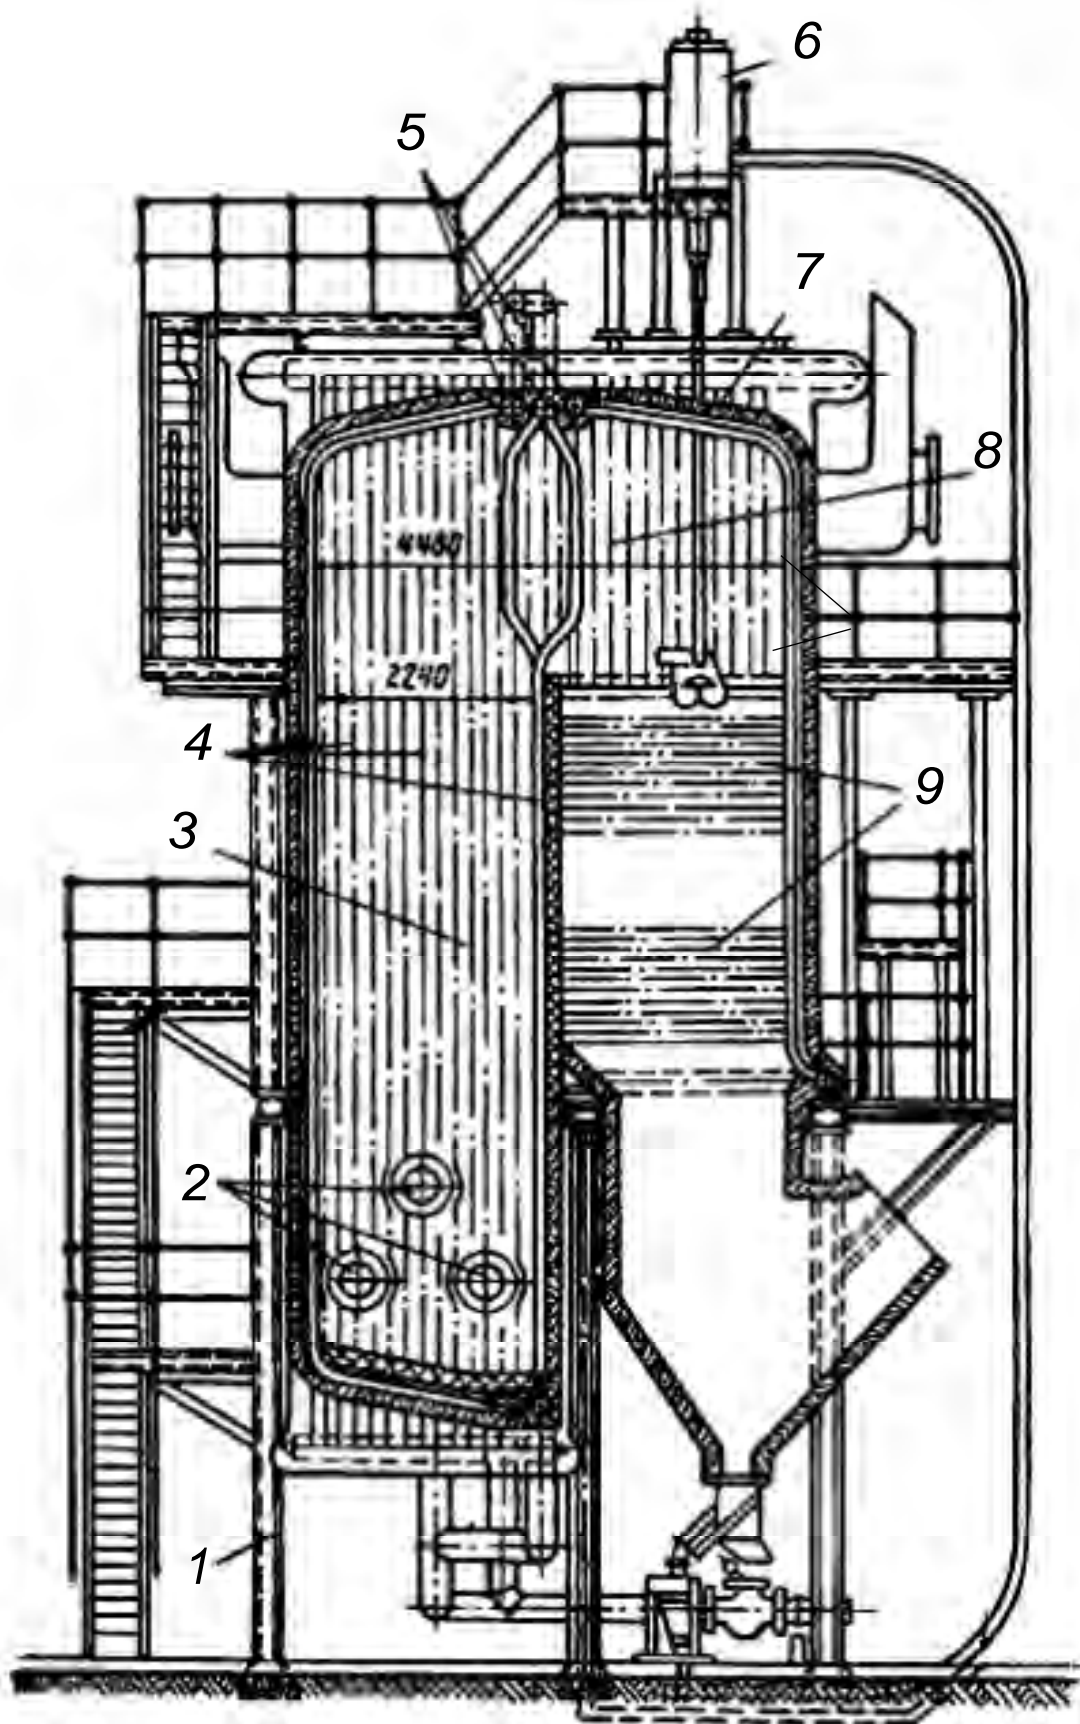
Водогрейный котел ПТВМ-30М: 1 – каркас; 2 – газомазутные горелки; 3 – топочная камера; 4 – трубы экранов; 5 – коллекторы; 6 – дробеструйная установка; 7 – обмуровка; 8 – поворотная камера; 9 – конвективные пакеты
